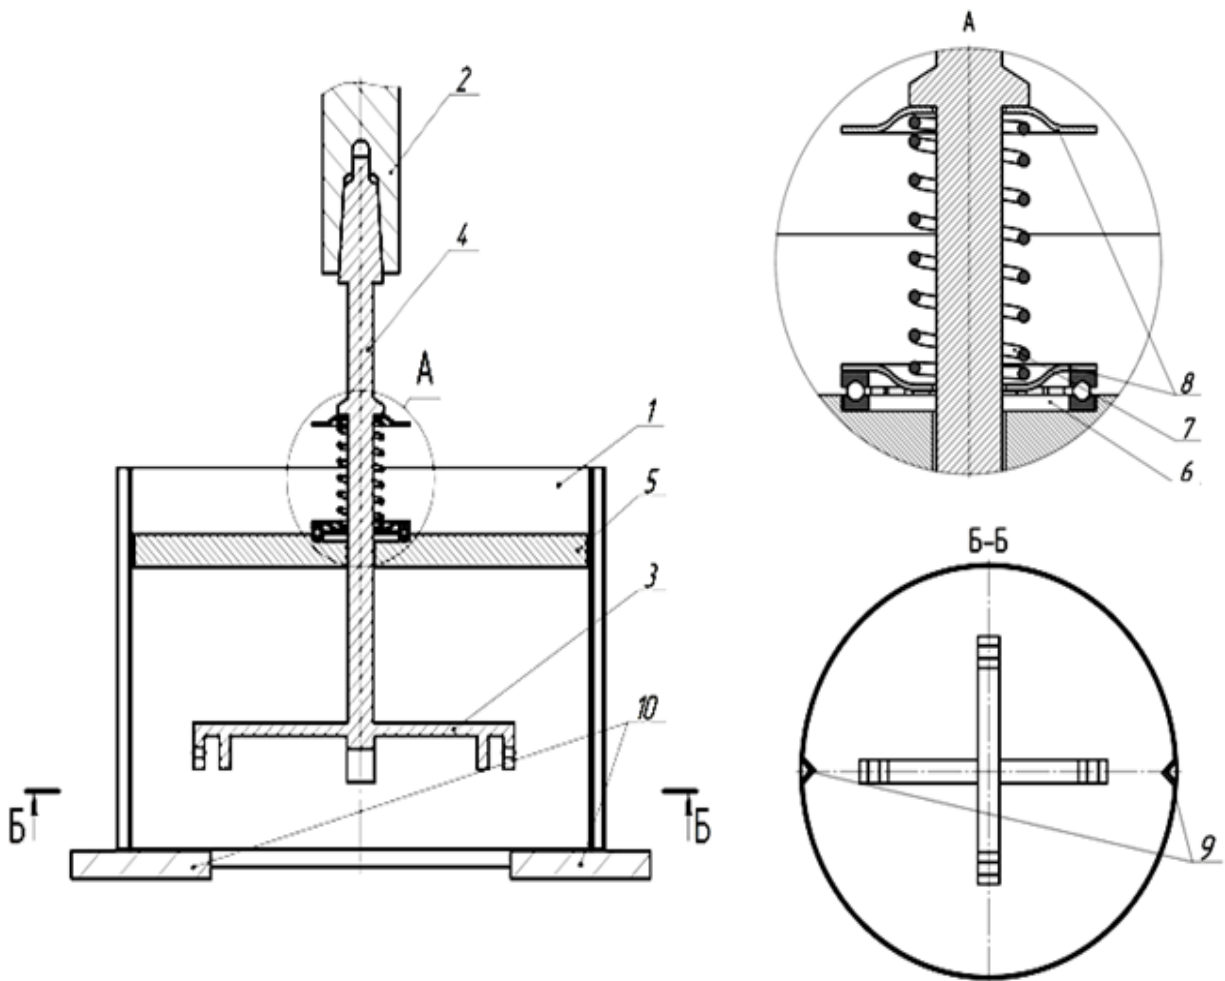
Общий вид установки для исследования износостойкости рабочих органов сельскохозяйственных орудий на базе вертикально-сверлильного станка
